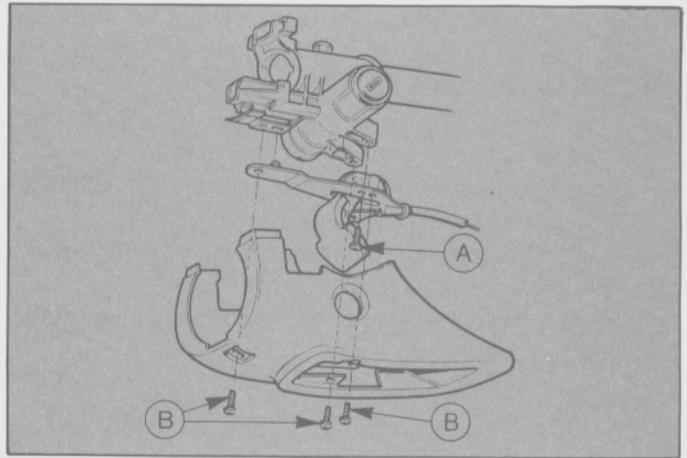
Palanca de desenganche del capó y cobertura de la columna de dirección.
